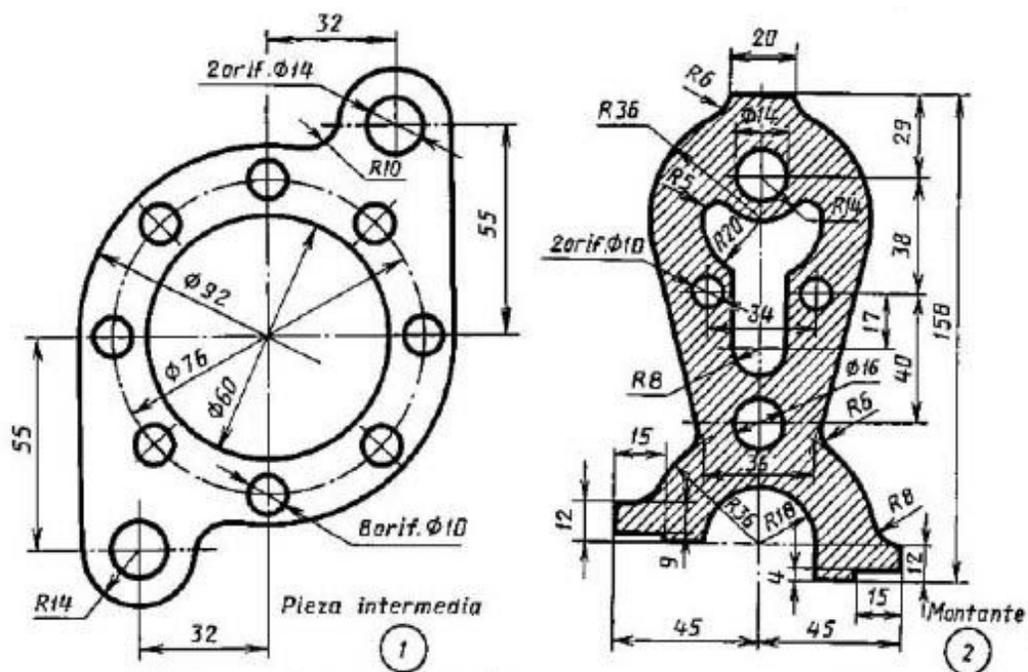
Pieza 1: Pieza intermedia; Pieza 2: Montante
